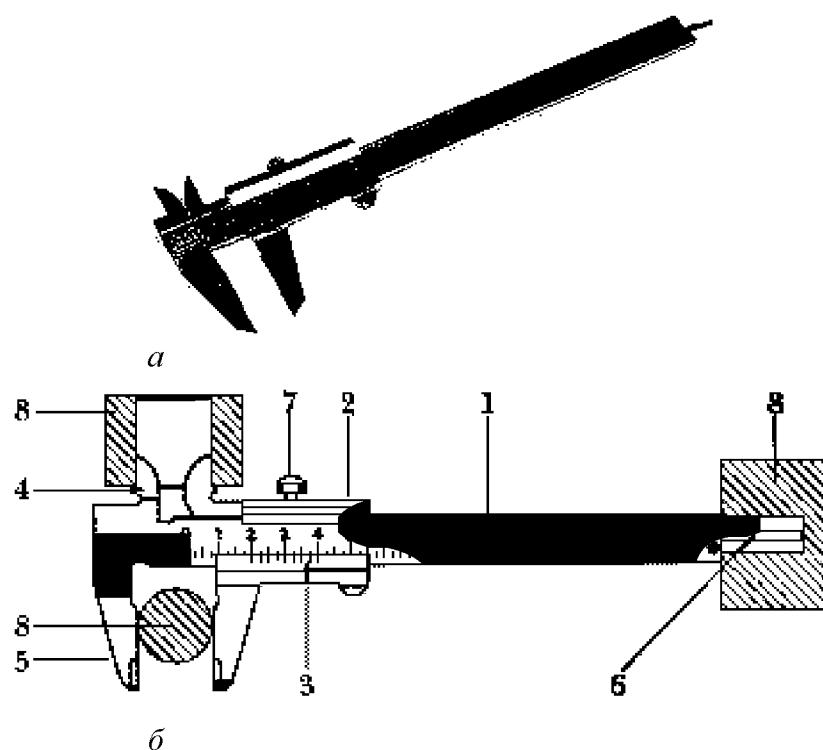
Штангенциркуль ШЦ-І: *а* – общий вид; *б* – схема измерения размеров:
